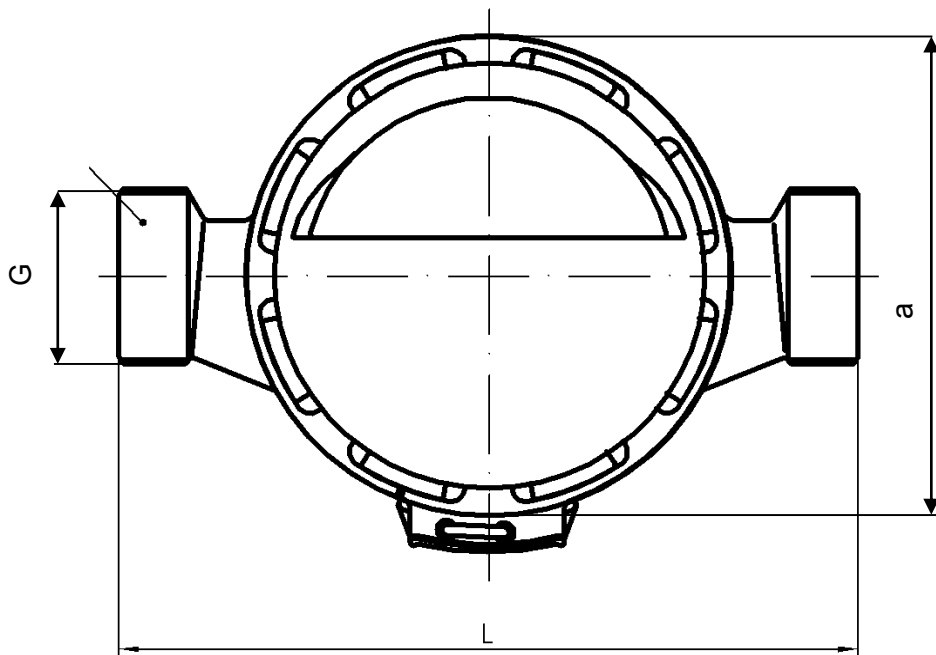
Габаритные и установочные размеры датчиков потока крыльчатых DN 15 и 20
